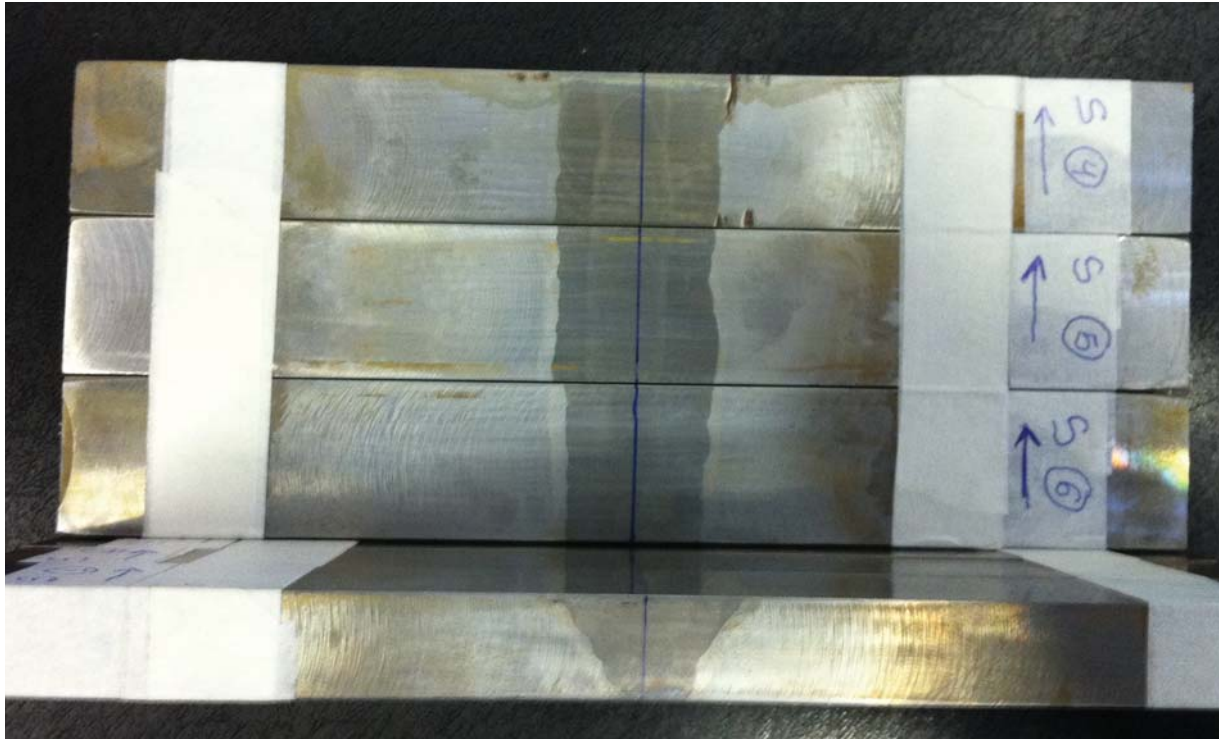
Corpos de prova SE (B) (solda) após o ataque químico – Seção transversal + Vista superior
